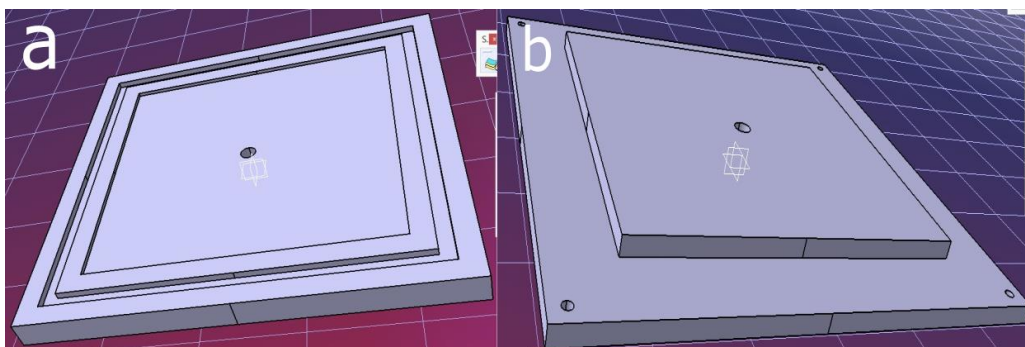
(a) Base del molde diseñado en CATIA. (b) Tapa/Punzón del molde.
